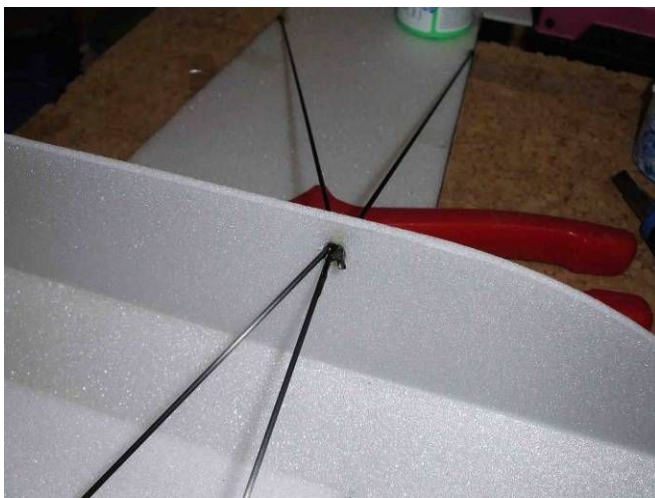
Verbindungspunkt der Tragflächenstreben am Rumpf
